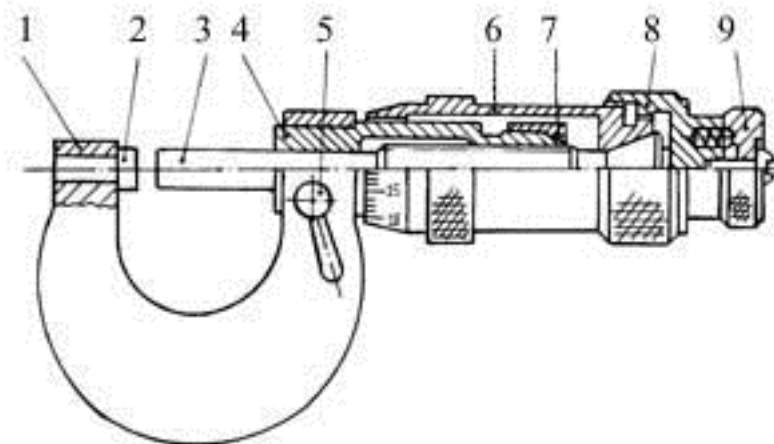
Строение гладкого микрометра: 1 – скоба; 2 – неподвижная пятая; 3 – микровинт; 4 – стембель; 5 – фиксатор; 6 – барабан; 7 – гайка; 8 – корпус храповика; 9 – храповик;
